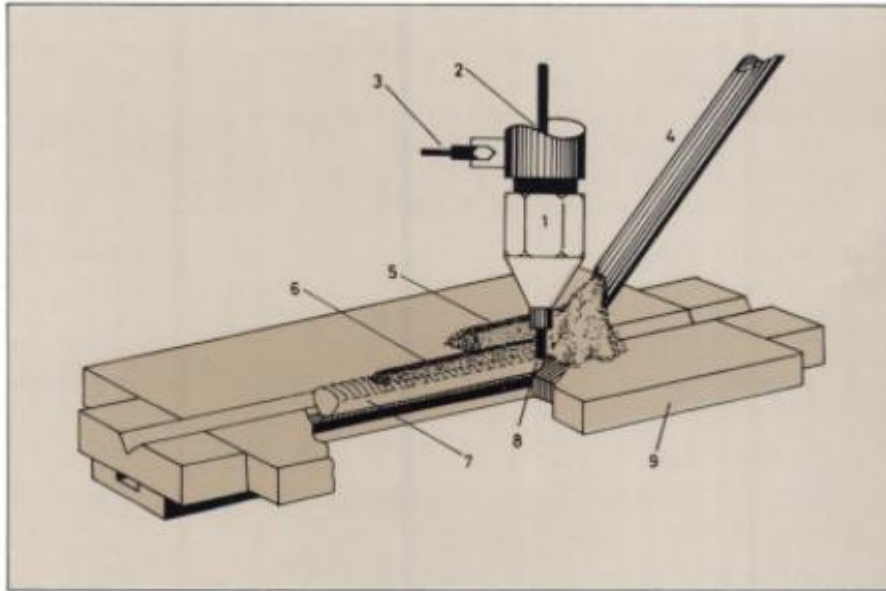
Soldadura por arco sumergido: 1) boquilla; 2) paso del alambre; 3) cable de alimentación de soldadura; 4) tipo de fundente; 5) fundente no fundido; 6) fundente fundido (escoria); 7) cordón de soldadura; 8) alambre electrodado; 9) material base o pieza de trabajo ^[8]
